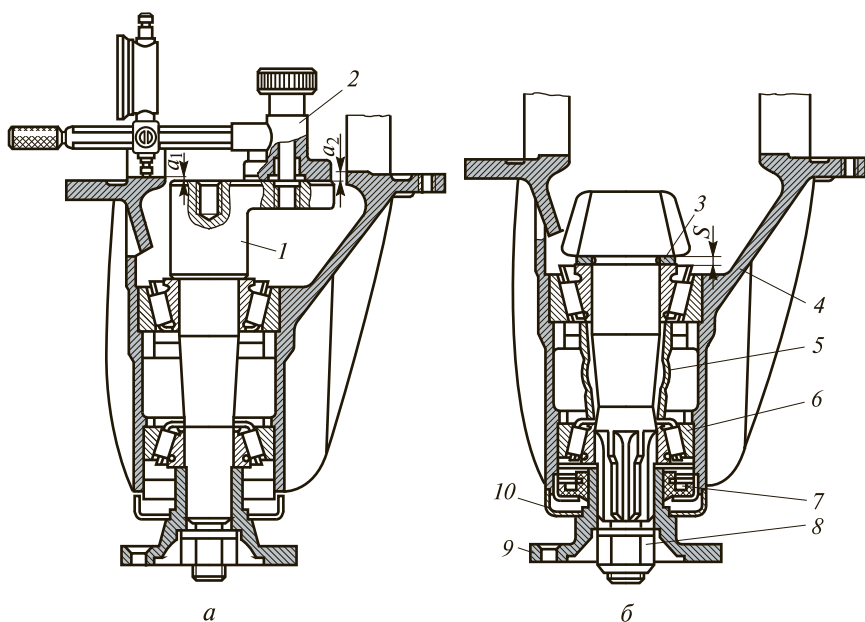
Схема установки шестерни оправки А.70184 и индикатора для определения толщины регулировочного кольца ведущей шестерни (а) и установка ведущей шестерни (б):
